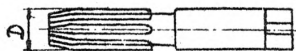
развертка ручная с цилиндрическим хвостовиком
